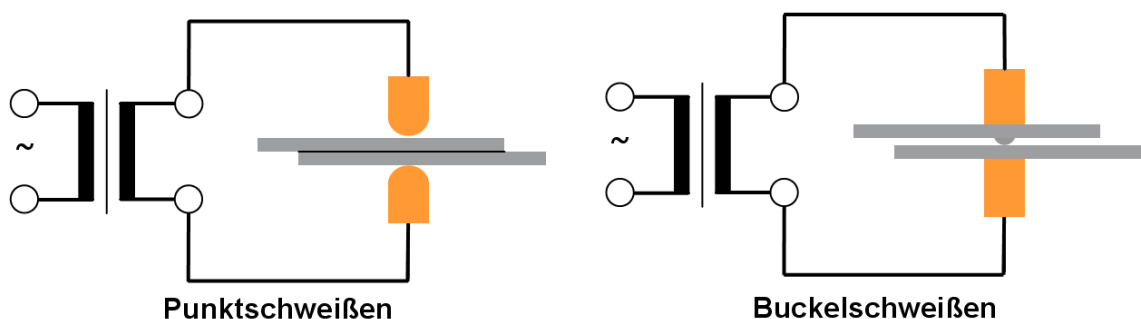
Vergleich Punktschweißen und Buckelschweißen [55]
